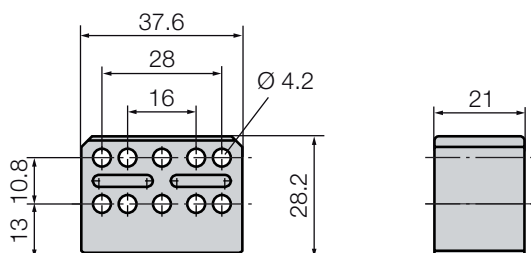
Dimensioni di ingombro datore di posizione BTL6-A-3800-2
